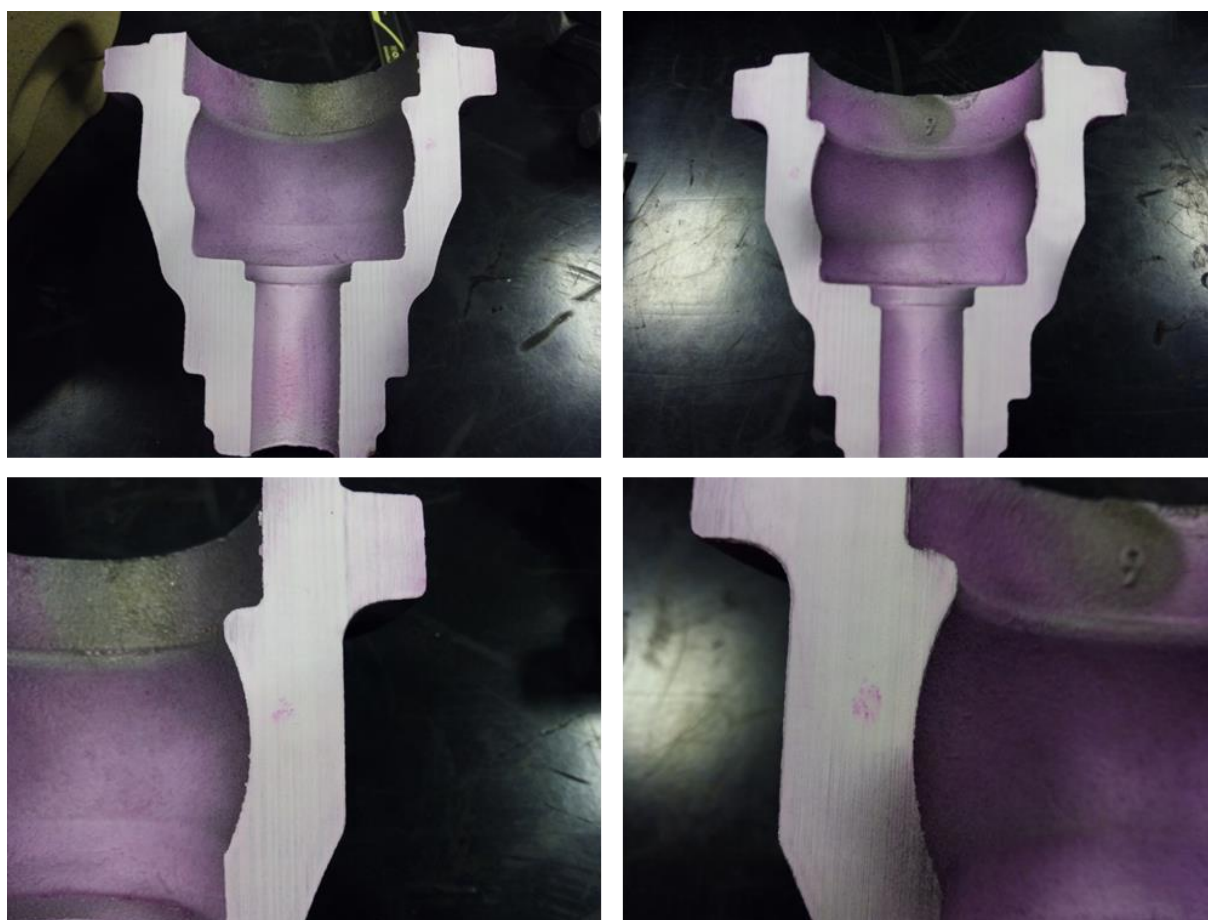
Foto da peça 2, cortada segundo o plano de separação, depois do ensaio de Líquidos Penetrantes.
